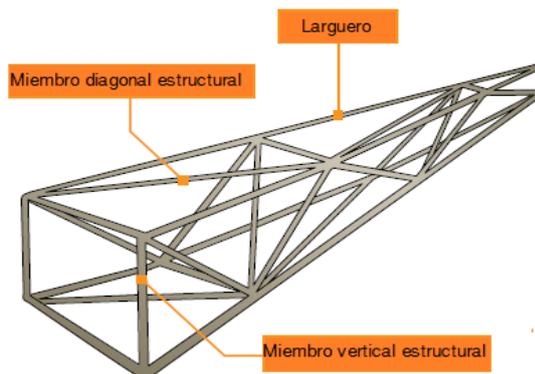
Fuselaje tipo truss, principales miembros estructurales
